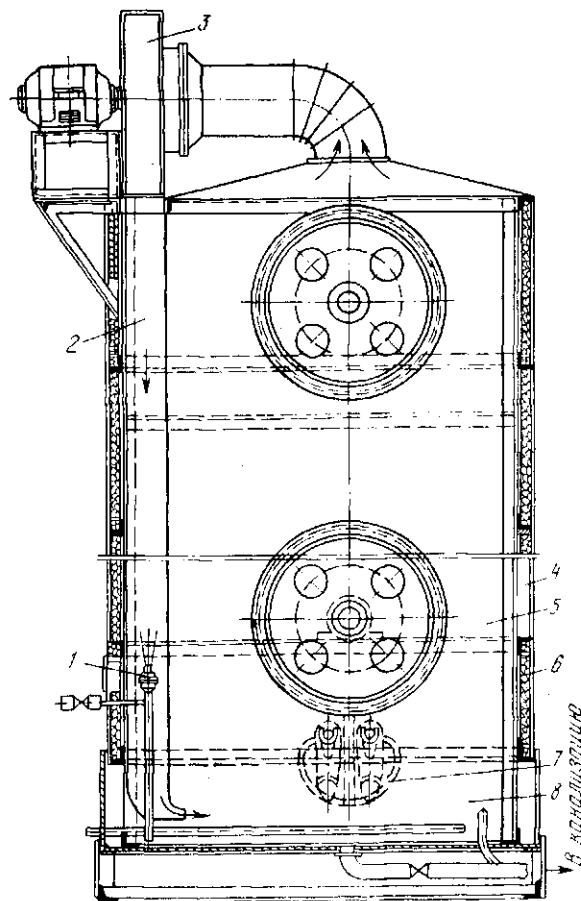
Схема элеваторной установки для увлажнения заготовок верха обуви влажным воздухом
